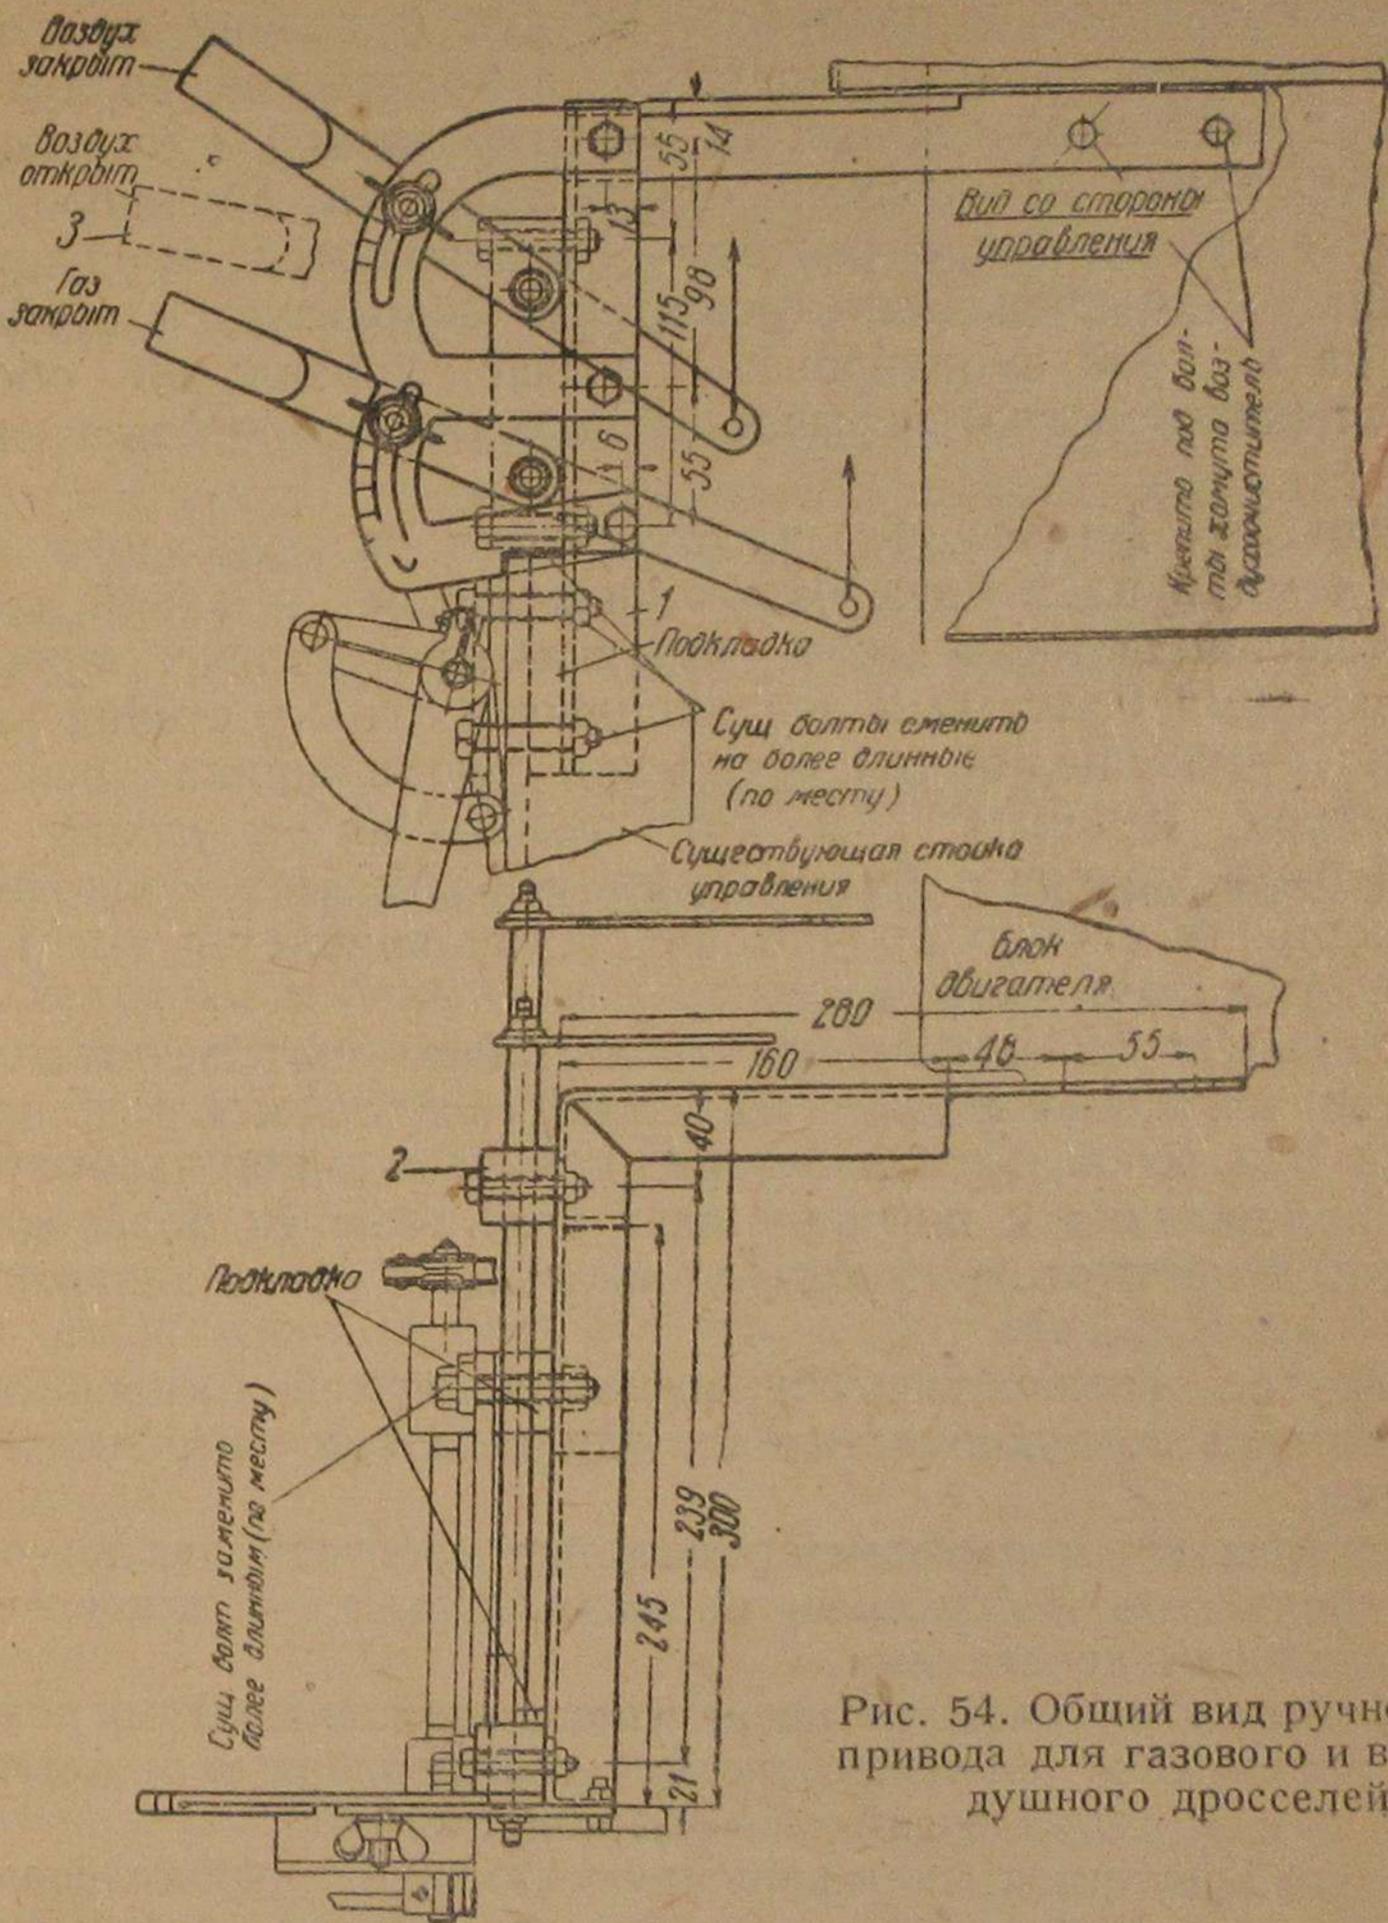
Общий вид ручного привода для газового и воздушного дросселей
